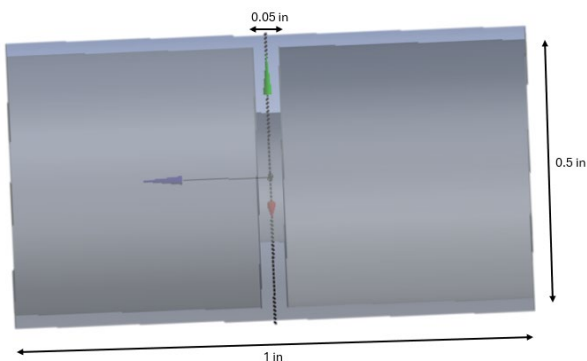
Geometría Propuesta de Accesorio de Tubería con Placa con Orificio.
